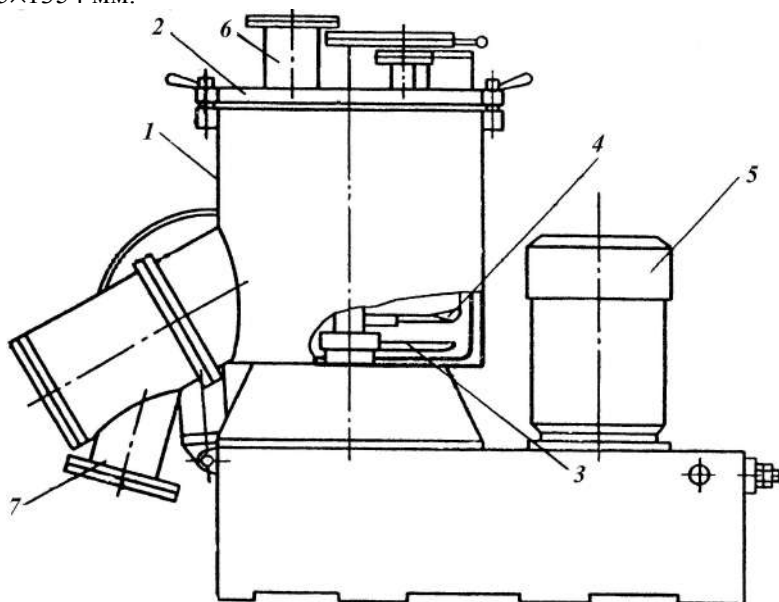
Смеситель циркуляционный центробежный типа ЦЛ: 1 – камера; 2 – крышка; 3 – мешалка в форме днища; 4 – лопастная мешалка; 5 – привод; 6 – загрузочный штуцер; 7 – разгрузочный клапан.
